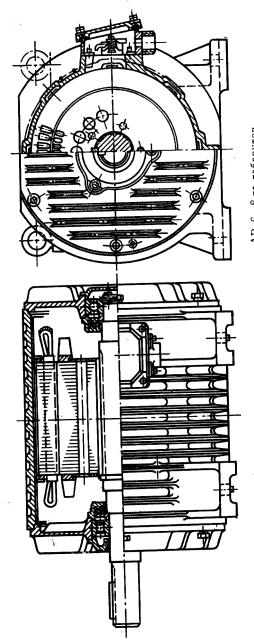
Общий вид рольгангового двигателя типа АР 6-8-го габаритов.
